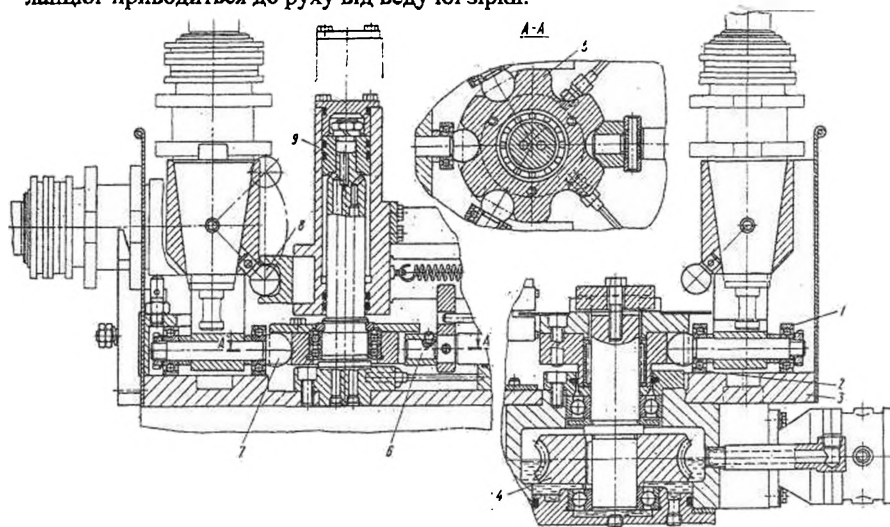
Ланцюговий інструментальний магазин з кантувачем
